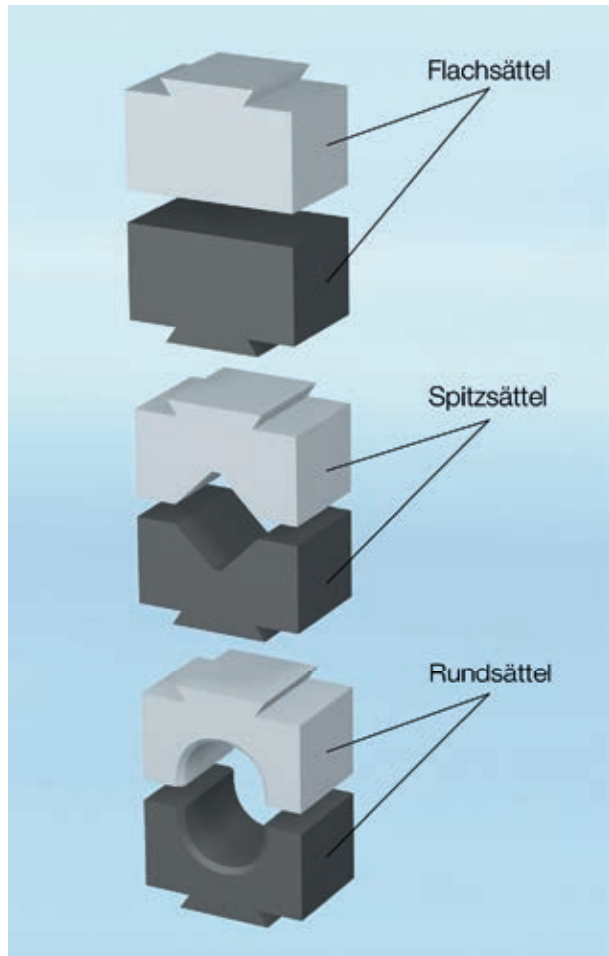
Sattelwerkzeuge für das Freiformschmieden
